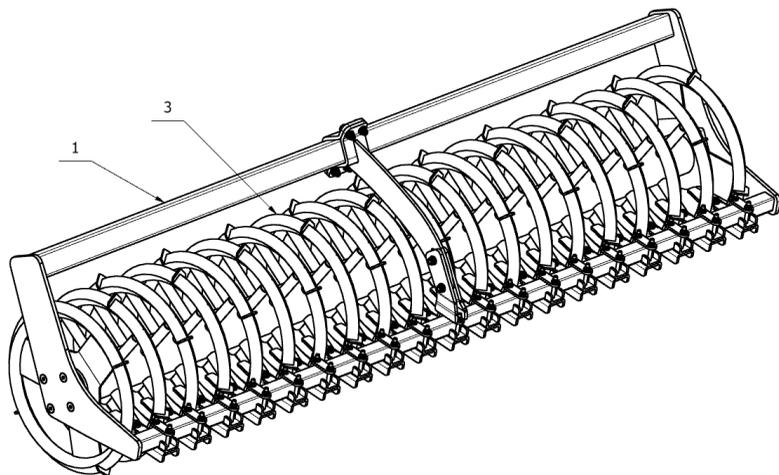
Dachwalze Plus Ø600mm auf Profil.
